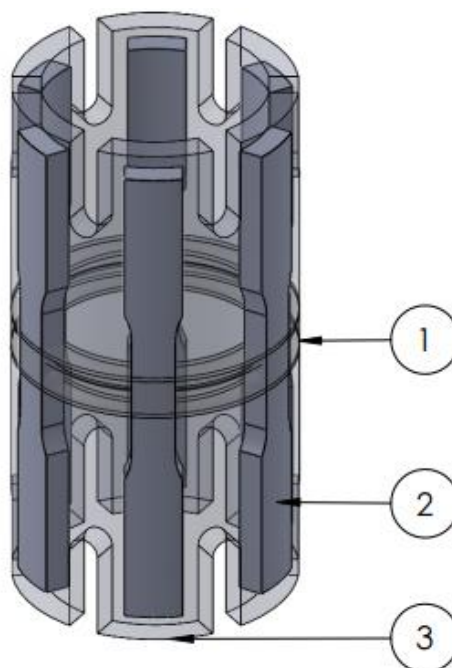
Desenho e dimensões em milímetros do anel rotatório.
